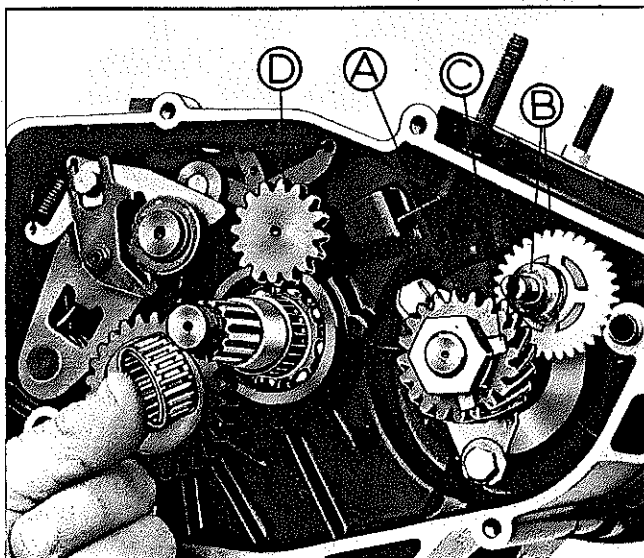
A. ENGRENAGEM DO VIRABREQUIM
